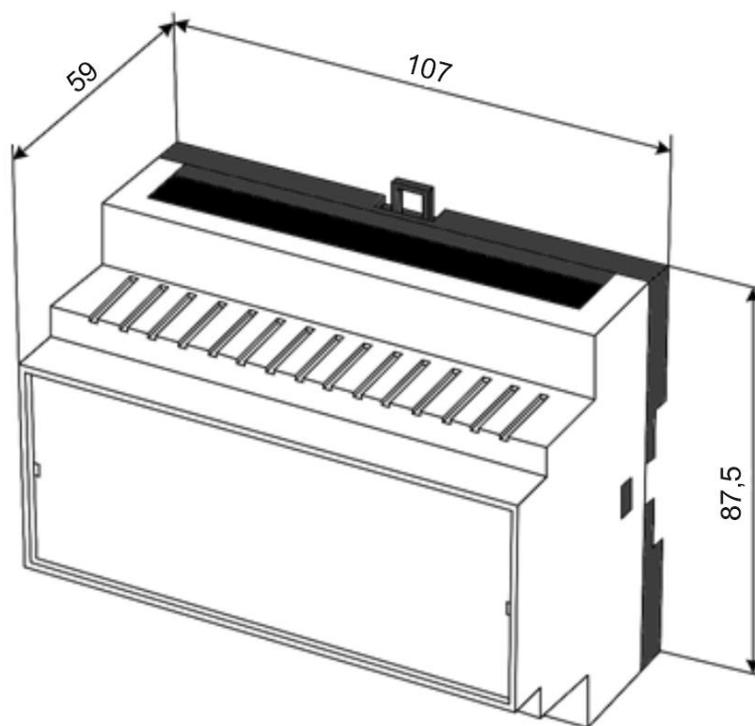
Габаритные размеры ВЭСТ-02М
